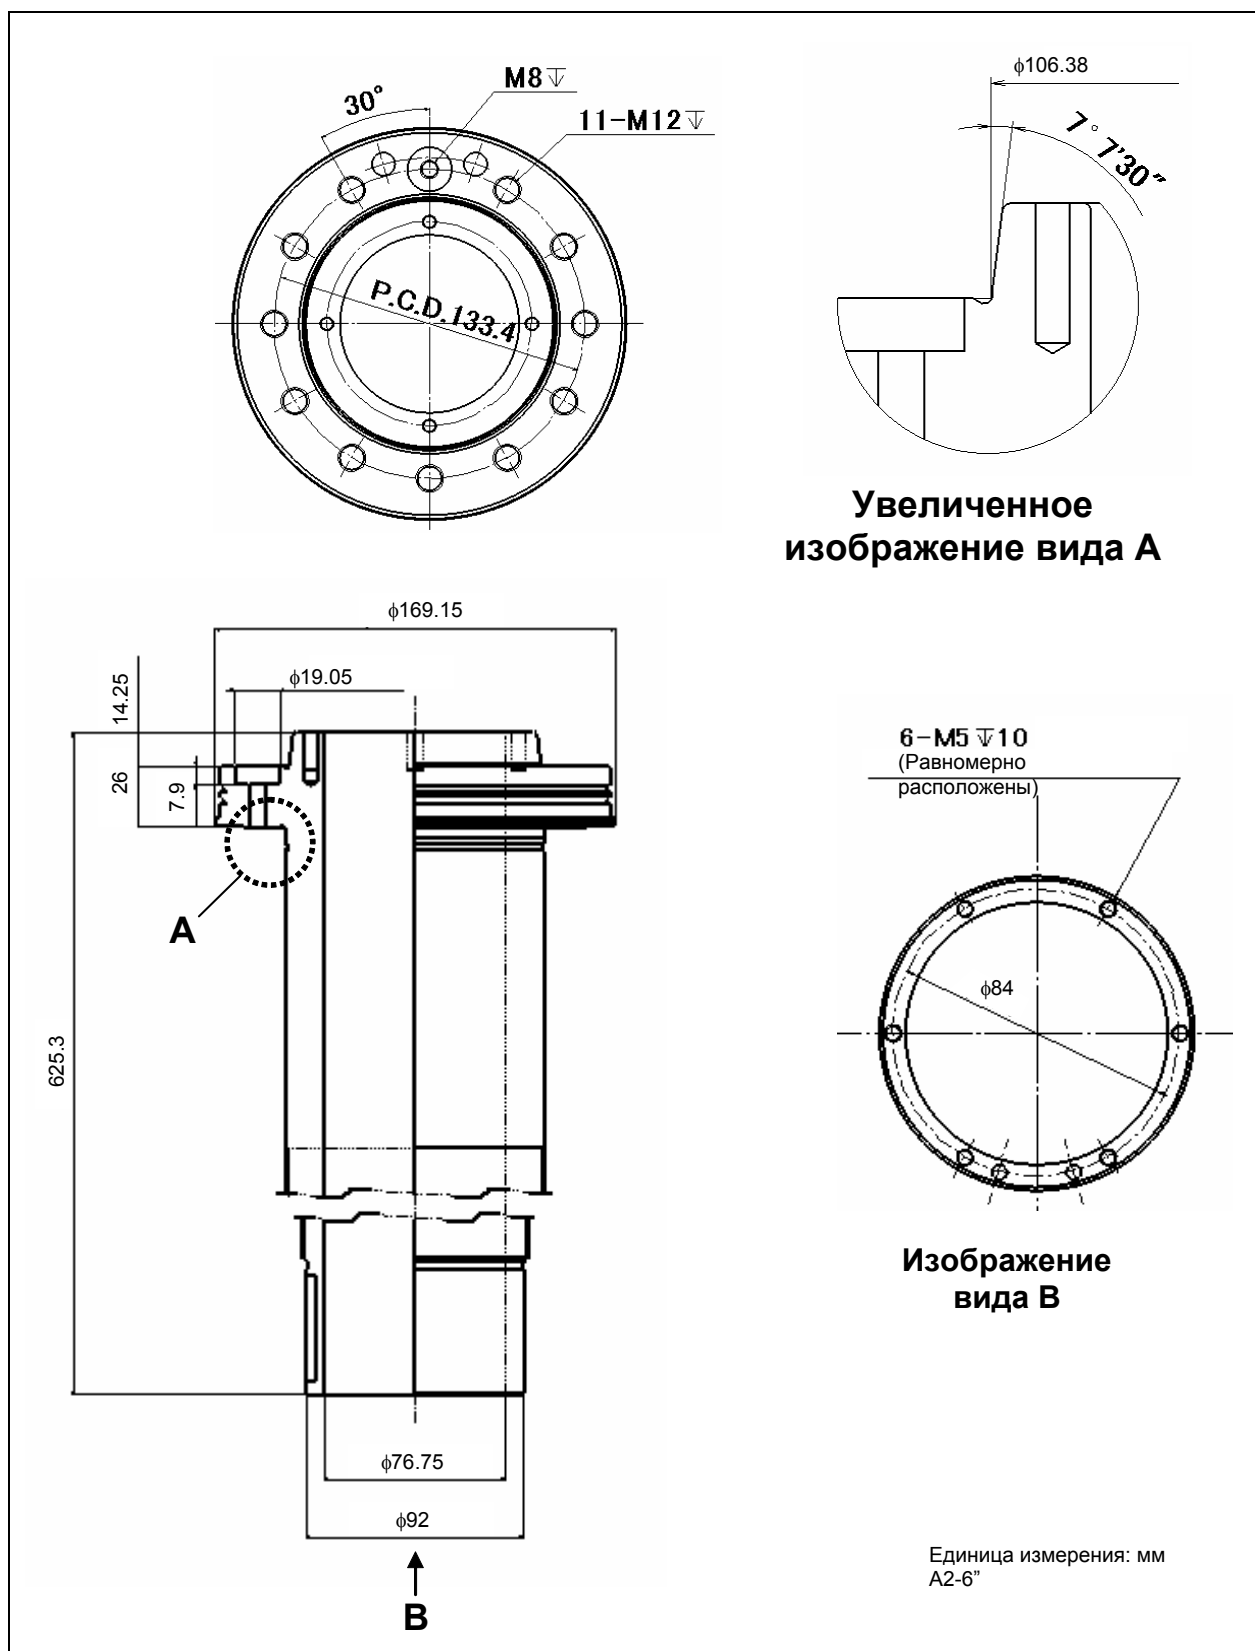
Чертёж торца токарного шпинделя (станка INTEGREX i-150 стандартной комплектации)
